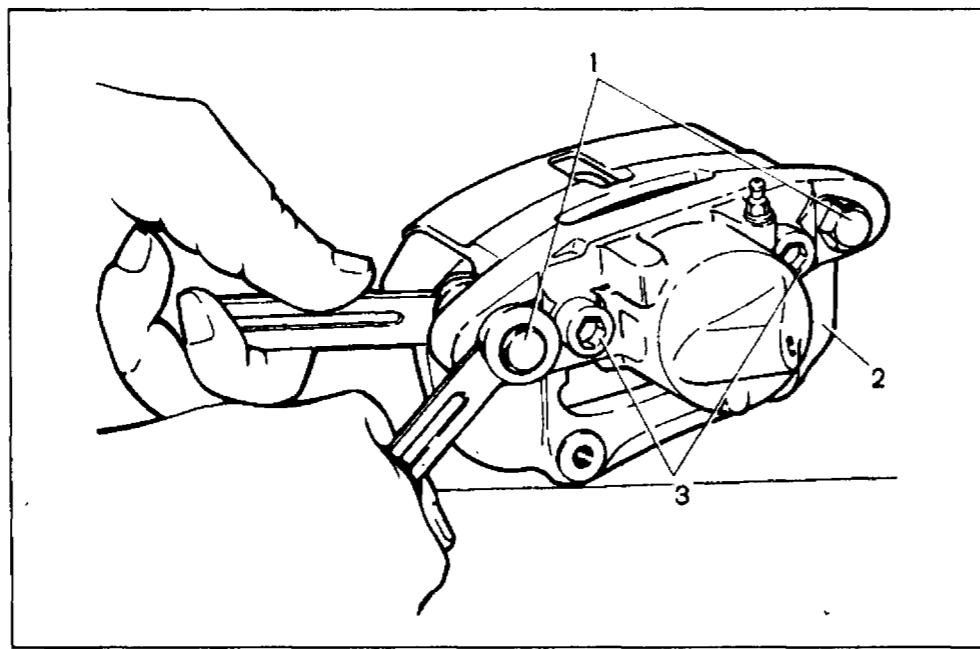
Отворачивание болта крепления цилиндра: 1 — болты крепления цилиндра; 2 — цилиндр; 3 — болты, стягивающие цилиндр с суппортом
